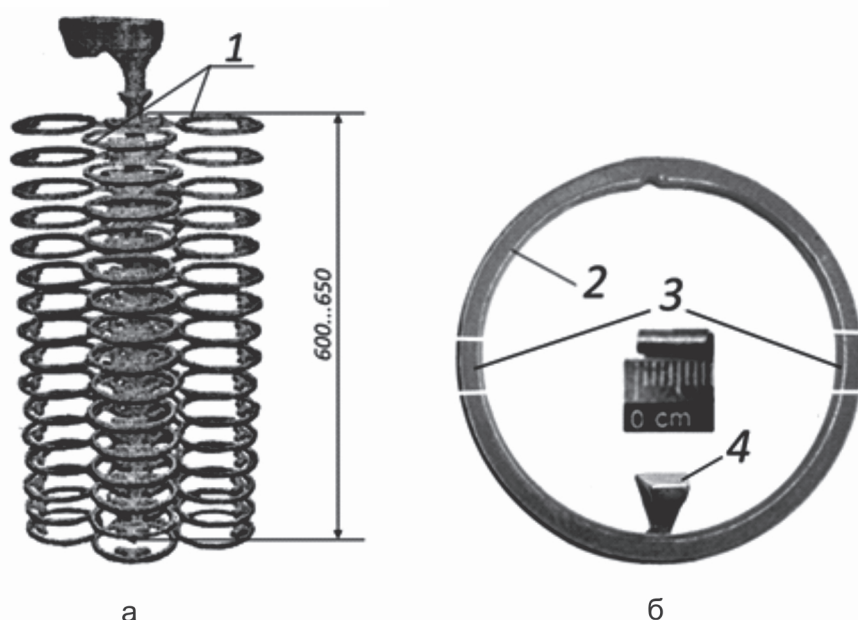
Виливки кілець-заготовок поршневих кілець: 1 – виливки після вибиття з ливарної форми [2]; 2 – виливок із зовнішнім діам. 130 мм; 3 – циліндричні зразки для газового аналізу та місця їх відбору; 4 – випор.
